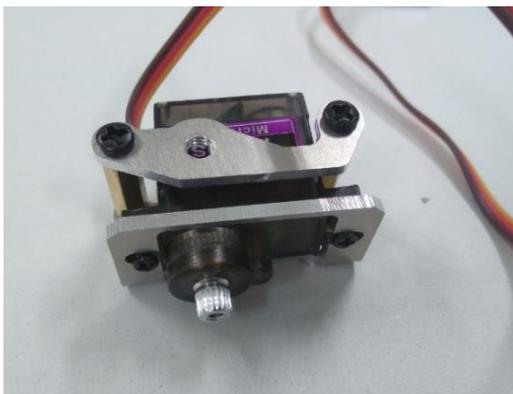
CONJUNTO PASO 15 VISTA 1
